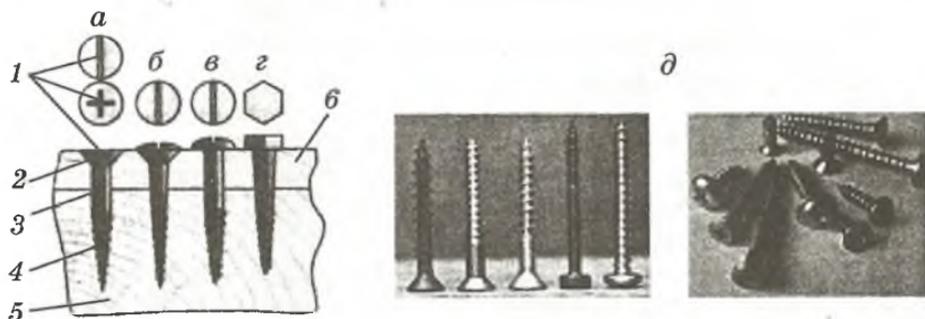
Виды шурупов по форме головки: *a* — потайная; *б* — полупотайная; *в* — полукруглая; *г* — шестигранная; *д* — общий вид: 1 — прорезь (шлиц), 2 — головка, 3 — стержень, 4 — винтовая нарезка, 5 — толстая основная деталь, 6 — тонкая деталь
